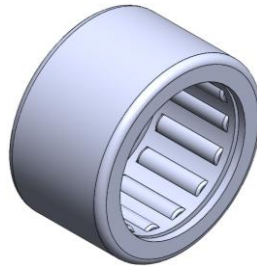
Modelo geométrico CAD 3D del rodamiento SKF HK 1512.
